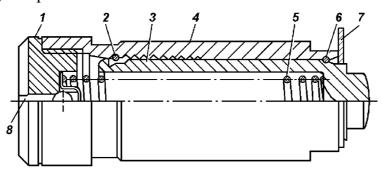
Гидронатяжитель с транспортным стопором:
